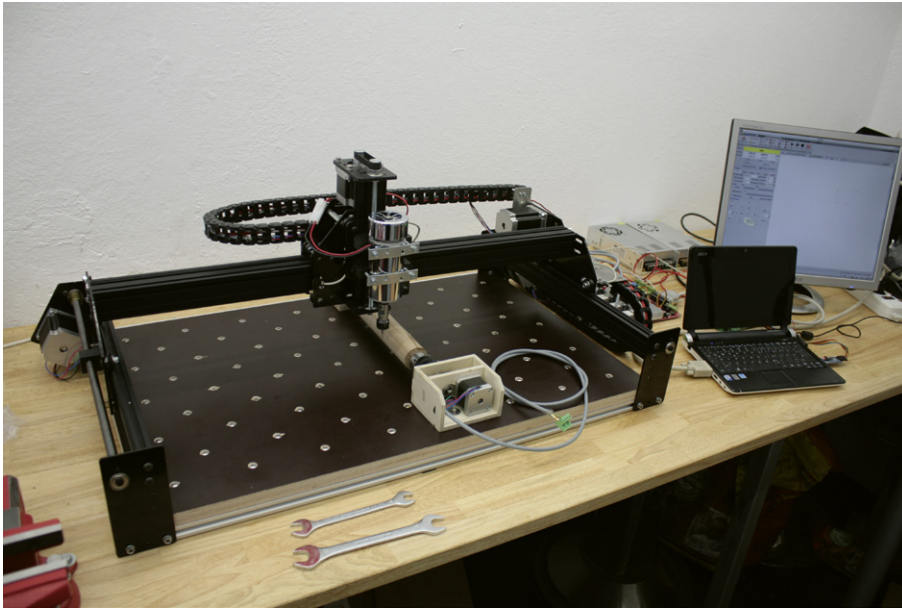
Größeres Kaliber: die Shapeoko-T mit Spindeltrieben, MaXYposi-Steuerung und vierter Achse
